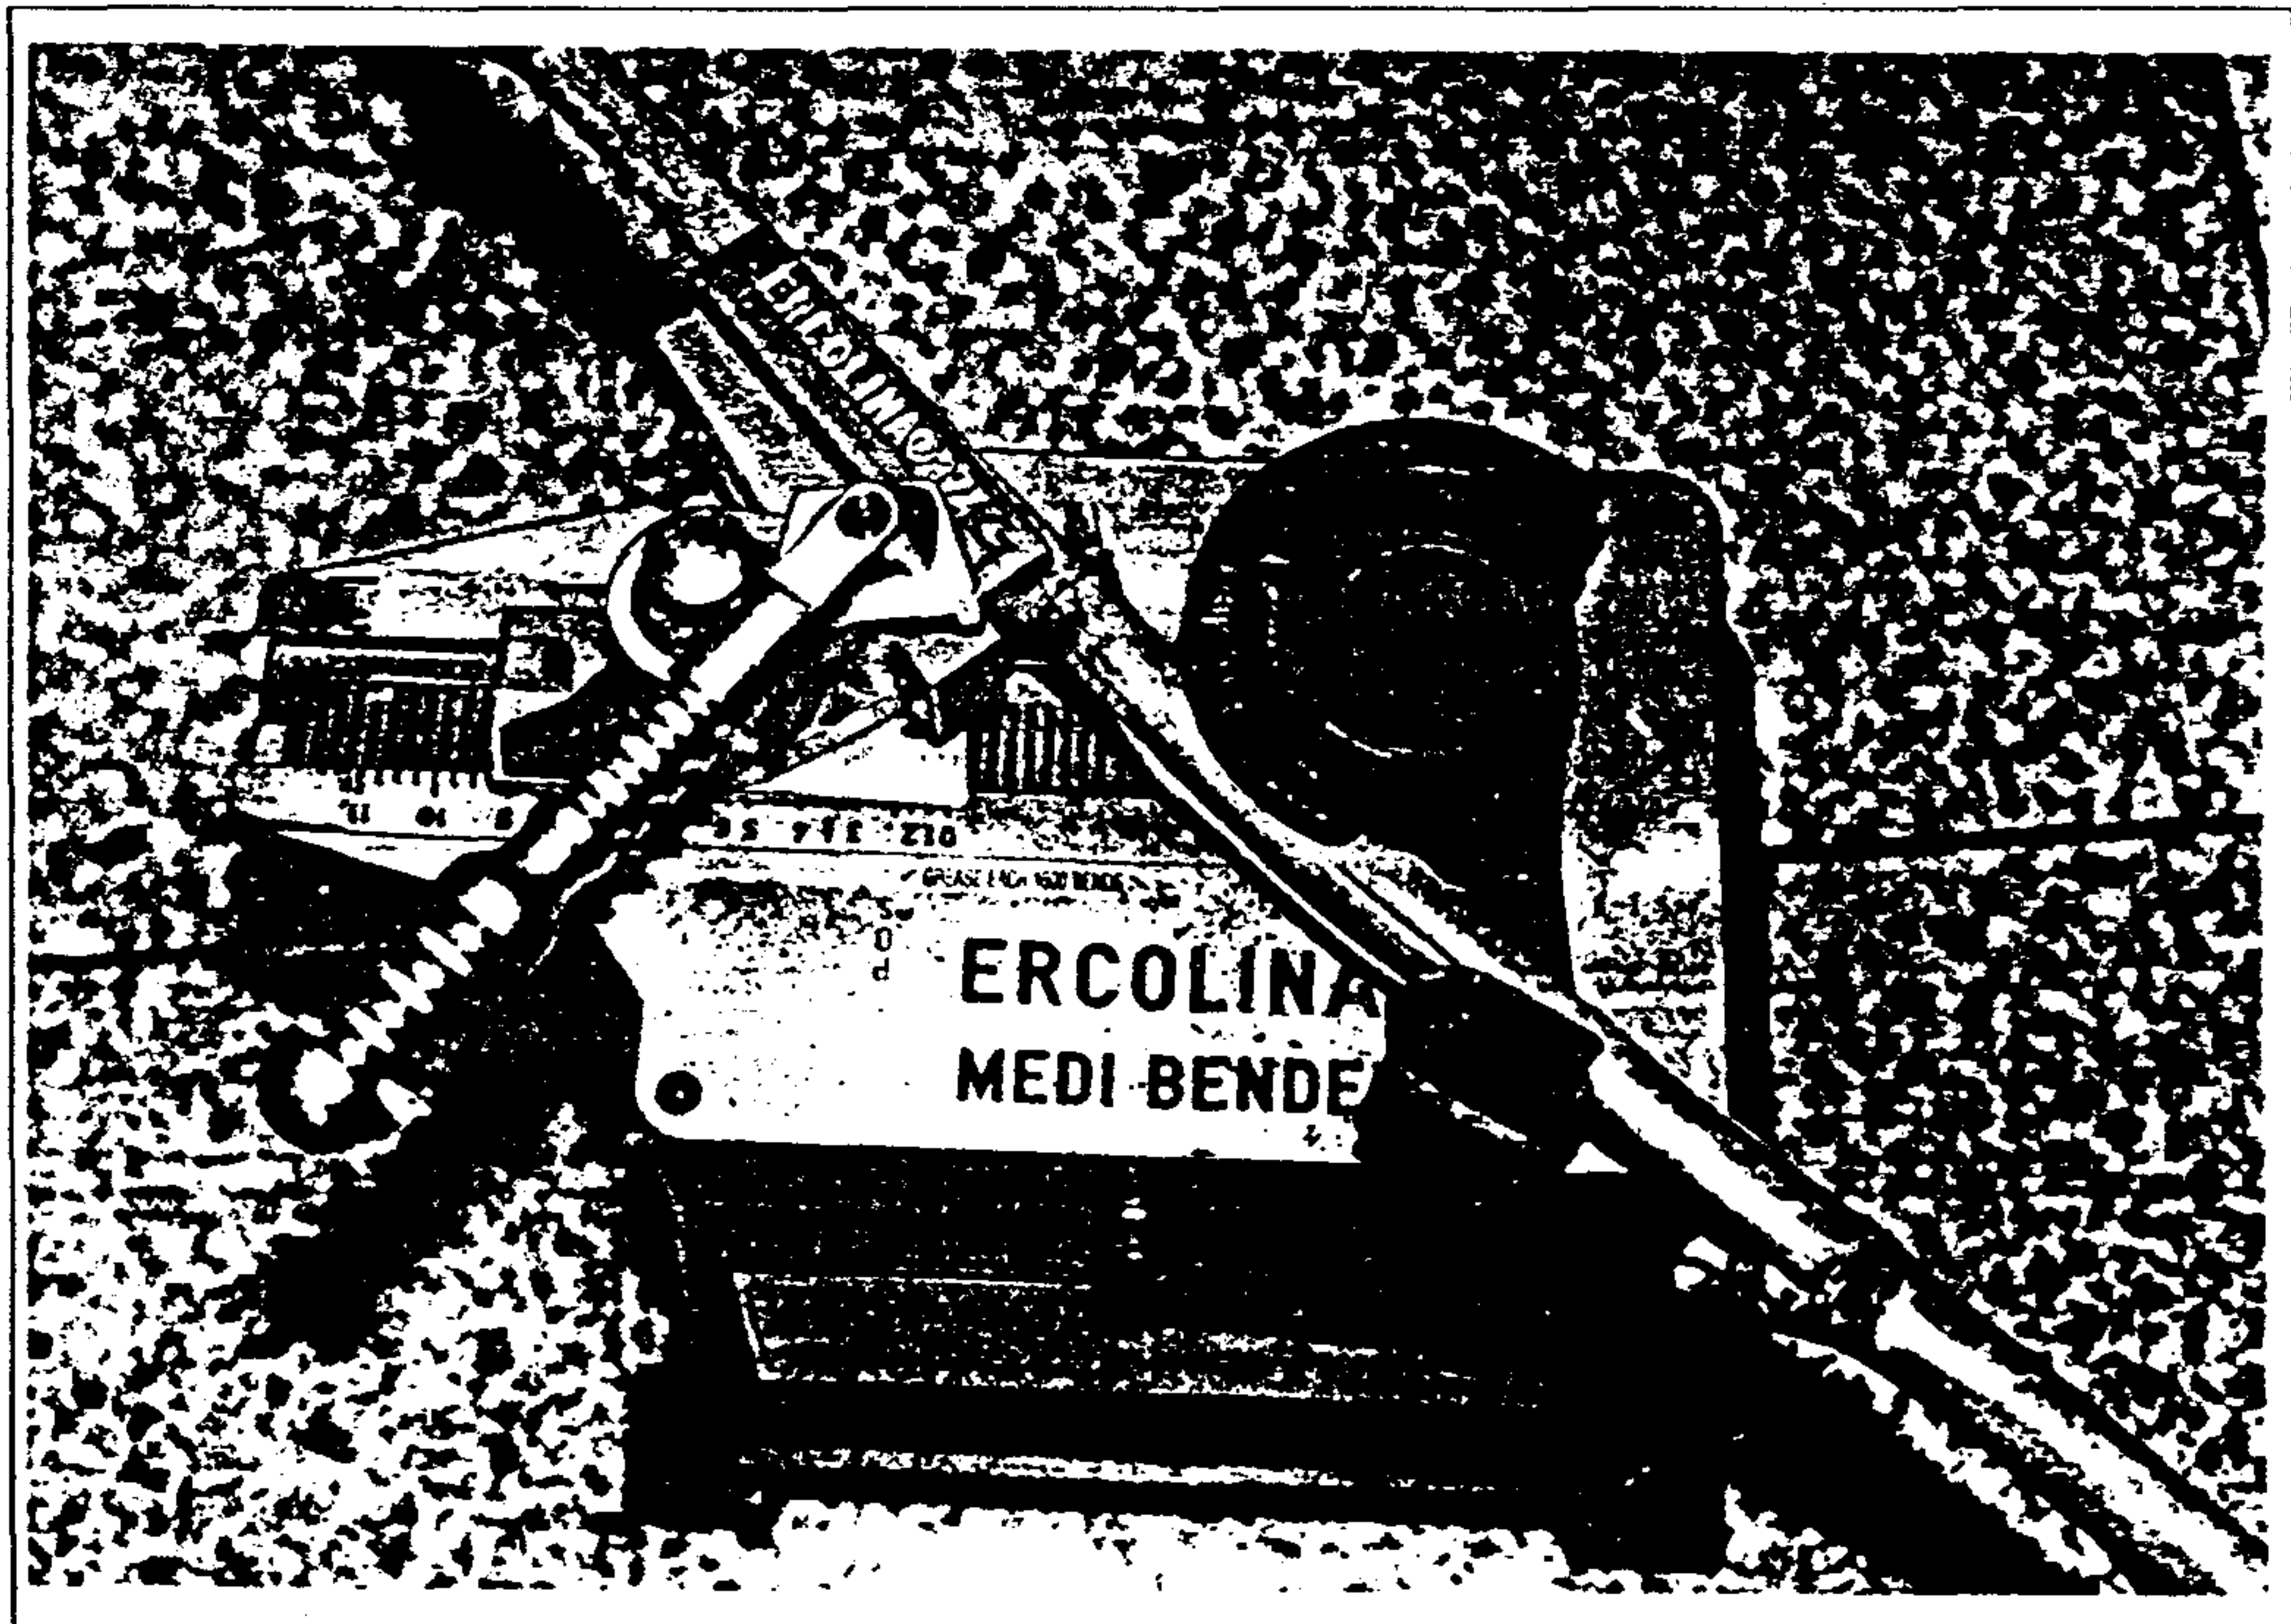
pipe bending machine을 이용한 원축 휩가공
